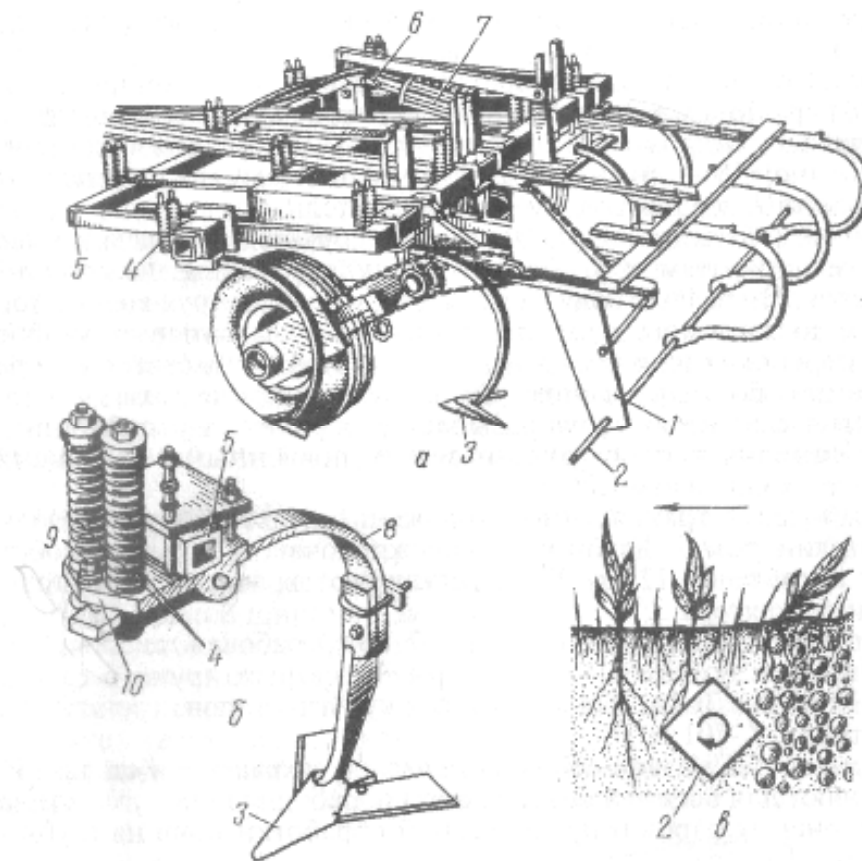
Культиватор КПЭ-3,8А со штанговым приспособлением:
